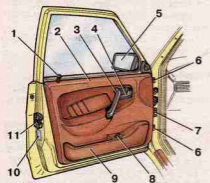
Внутренний вид передней двери: 1 — кнопка выключения замка; 2 — обивка двери; 3 — ручка подлокотника; 4 — внутренняя ручка двери; 5 — наружное зеркало заднего вида; 6 — болты крепления двери; 7 — ограничитель открывания двери; 8 — выключатель электростеклоподъемника; 9 — карман обивки двери; 10 — катафот; 11 — наружный замок двери
